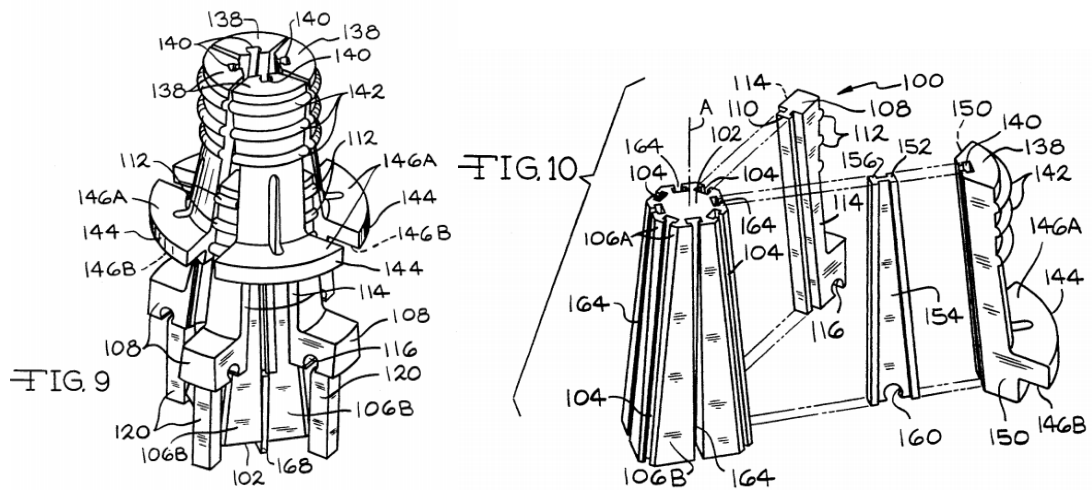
Patent, Mechanically Collapsible Core For Injection Molding
